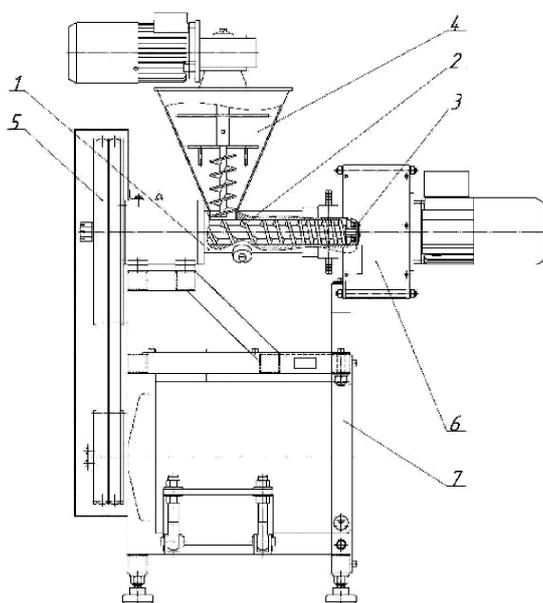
Экструдер Ш12-РЭК: 1 — корпус; 2 — шнек; 3 — фильера; 4 — шнековый питатель; 5 — привод шнека; 6 — нож с приводом для обрезки гранул; 7 — рама
